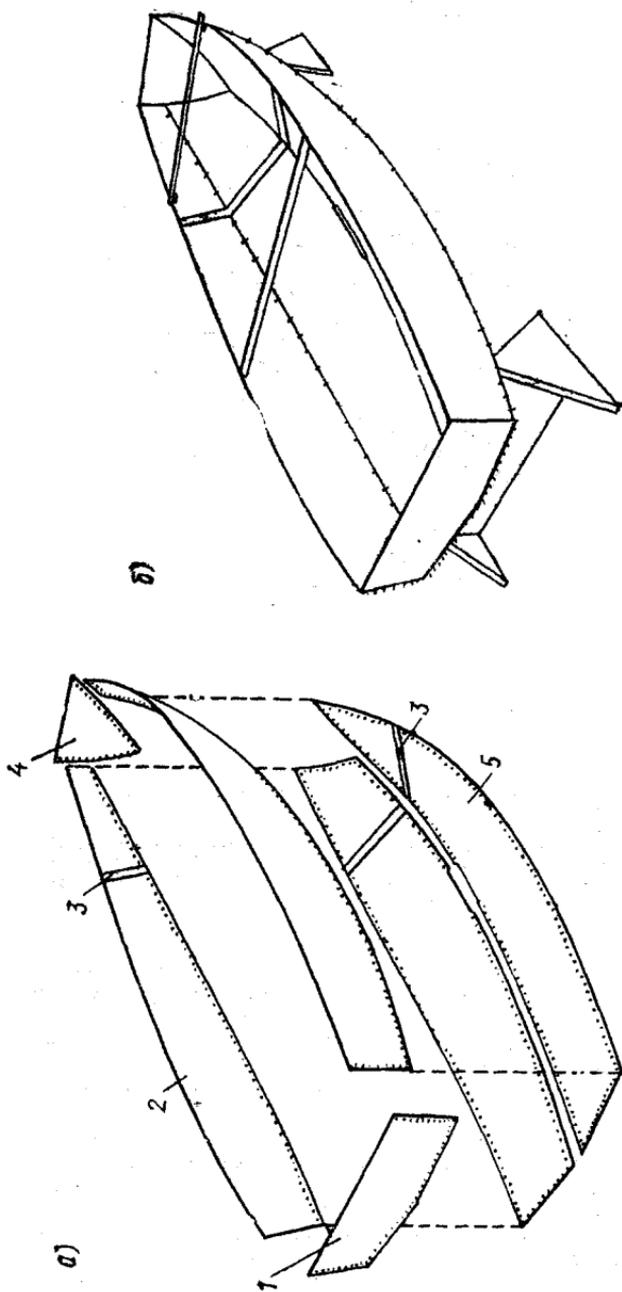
Заготовки фанерной обшивки (а) для бесстальнойной сборки швертбота «Миррор Динги» и «сшитый» на проволочных скрепках корпус (б) с поперечными распорками.
